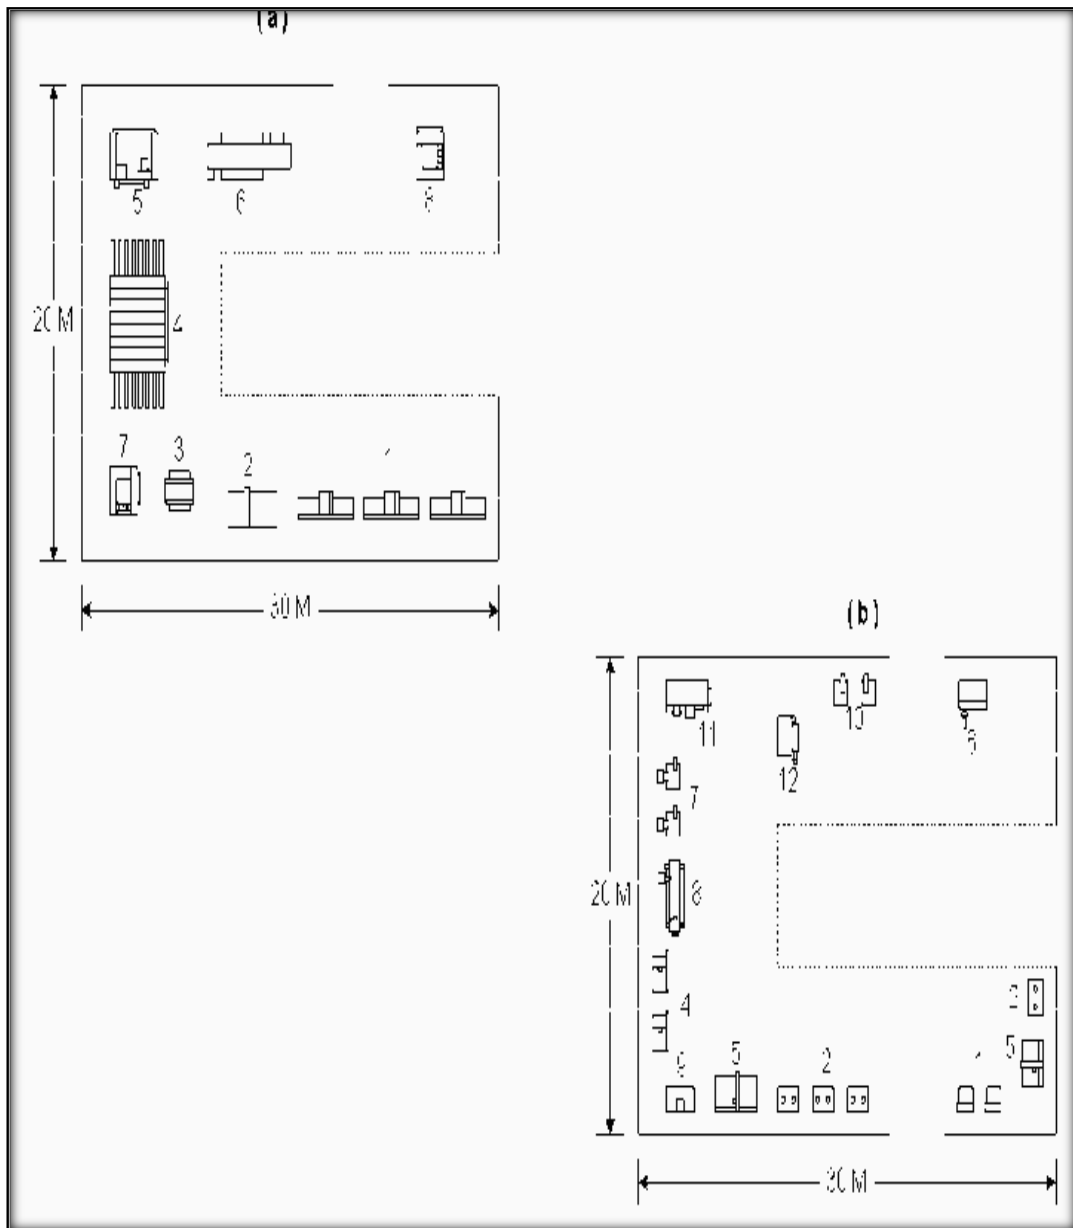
Distribución de la planta para fabricación de muebles de madera.
